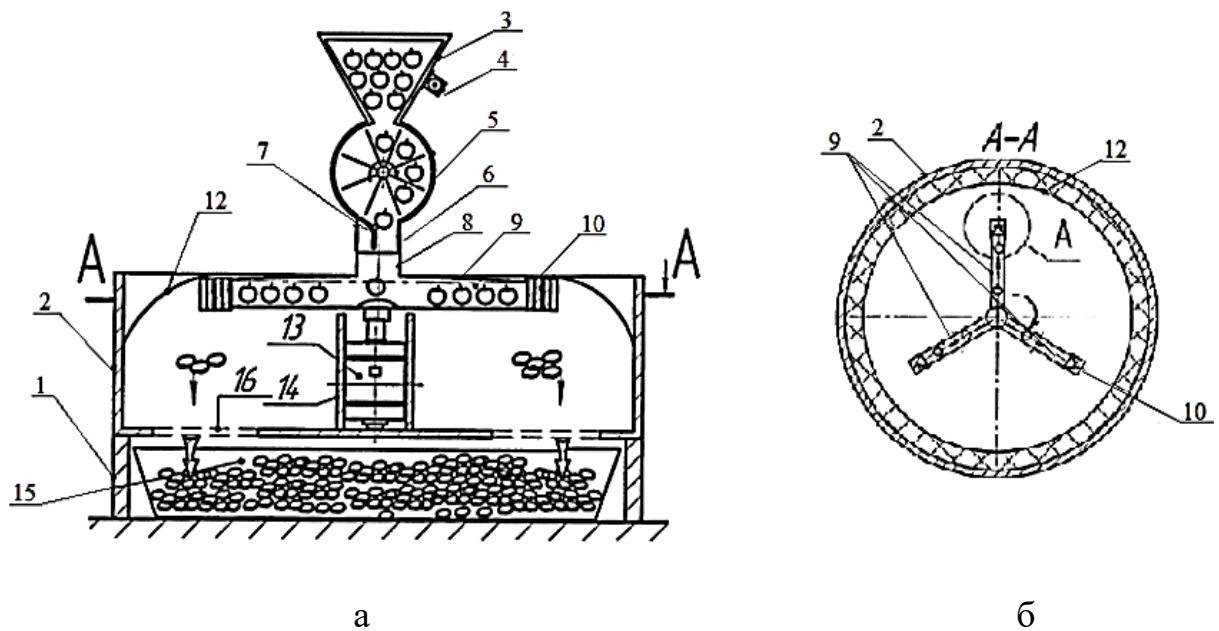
Подрібнювач плодоовочевої сировини, загальний вигляд; б - роторний подрібнювач плодоовочевої сировини, розріз А-А 1 – опори; 2 – циліндричний корпус; 3 – завантажувальний бункер; перекидний клапан, 8 – відцентровий ротор, 9 – напрямні труби; 10 – змінні ножові стінки; 11 – ножі; 12 - відбивачі; 13 – електродвигун; 14 – захисний кожух; 15 - ємність; 16 - вивантажувальні отвори
